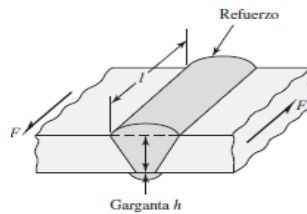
Dimensiones de una soldadura a tope sujeta a una carga cortante [31].
